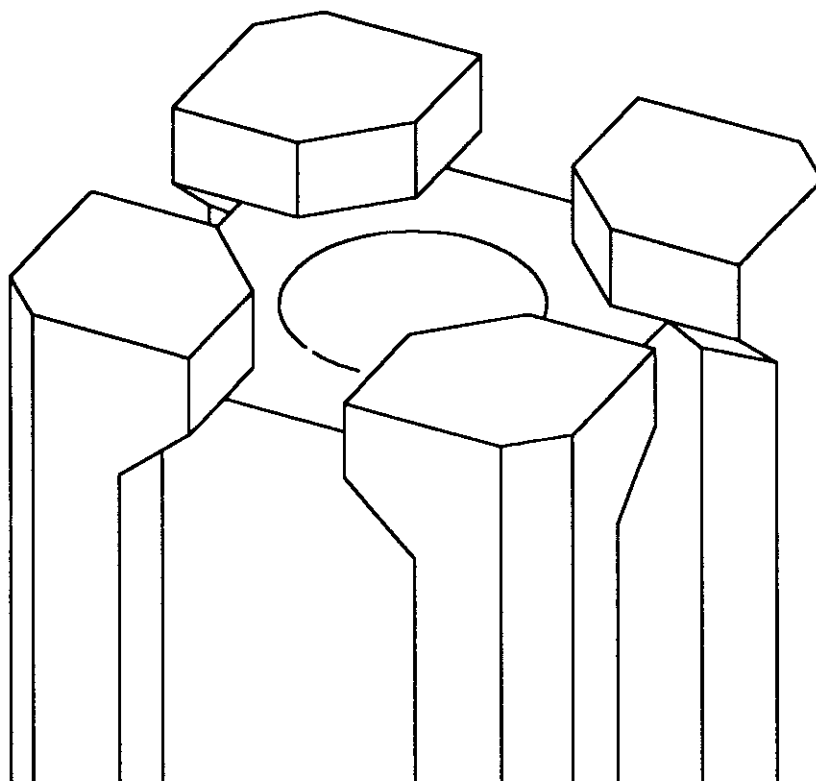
Detalhe da região superior dos pilares onde, devido à redução da seção transversal, existem altas tensões de contato.
